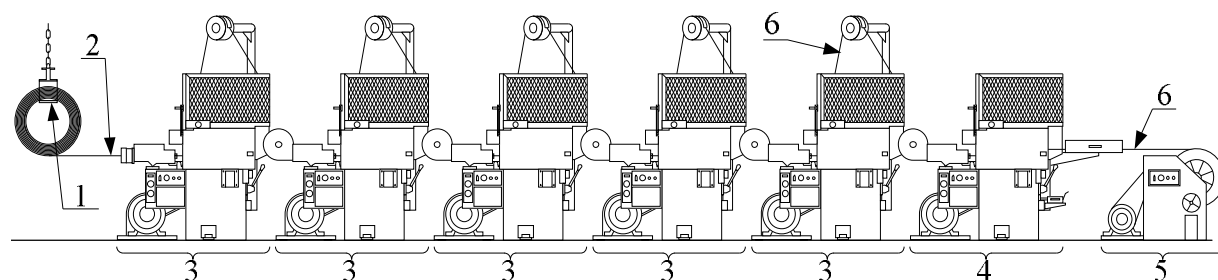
Волочильный стан поводкового типа: 1 – устройство для размотки бунтов заготовки проволоки; 2 – заготовка проволоки; 3 – блок предварительного волочения проволоки; 4 – блок для волочения готовой проволоки; 5 – намоточное устройство; 6 – проволока
